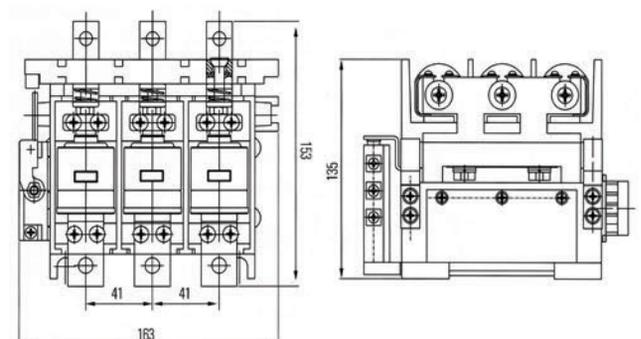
Габаритные размеры КВТ-1,14-80/125/160
